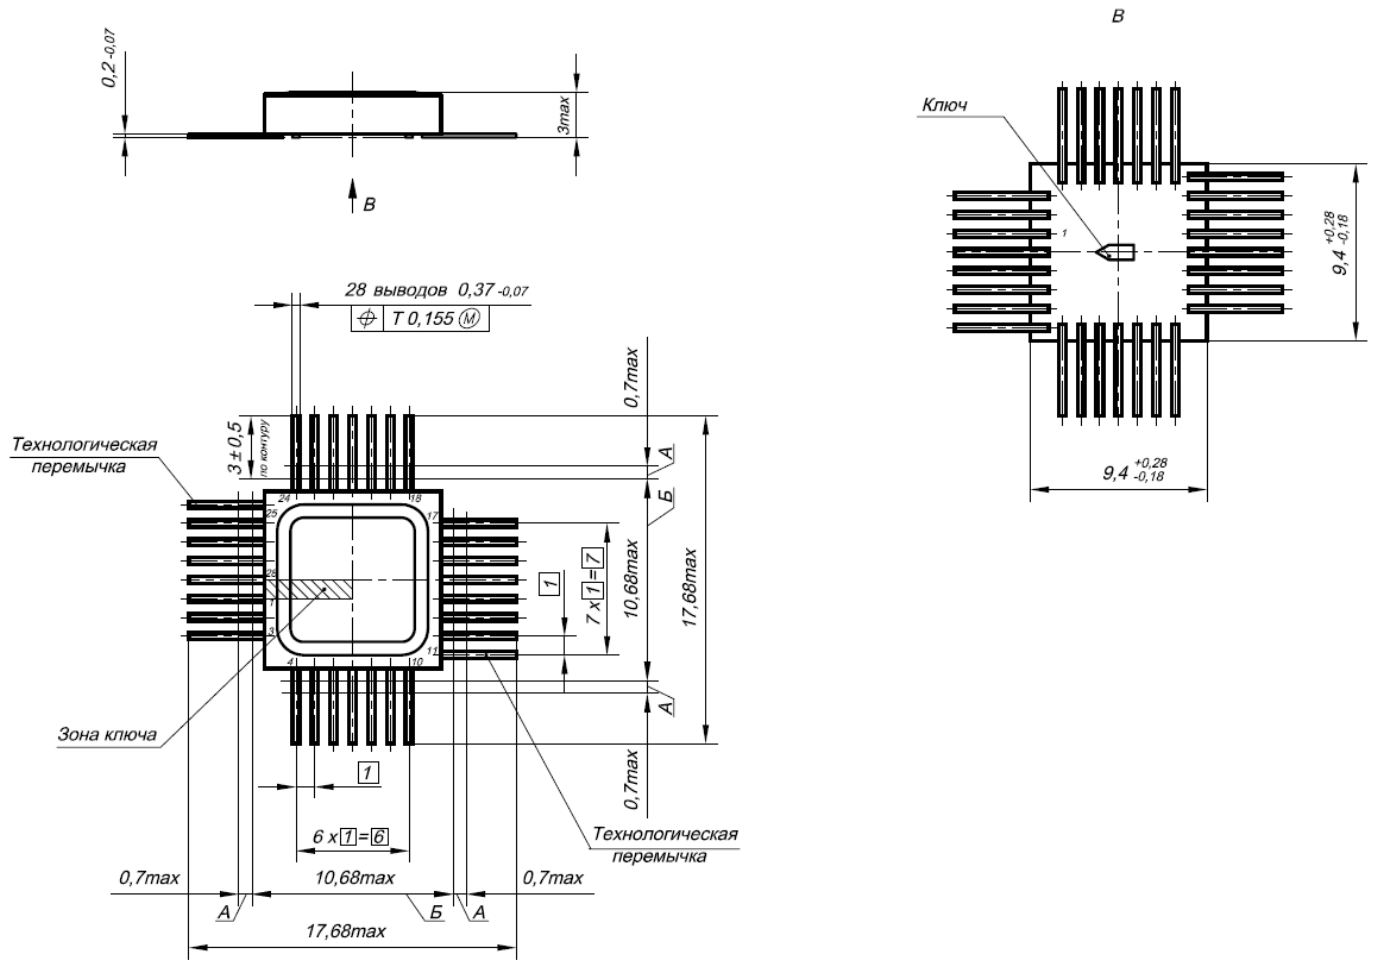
Габаритный чертеж корпуса Н09.28-1В
